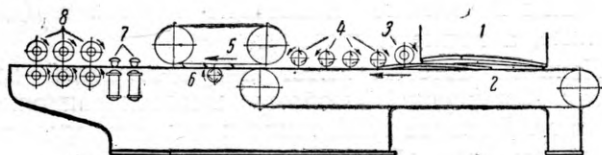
Агрегатный станок для окончательного фрезерования лыжных заготовок
